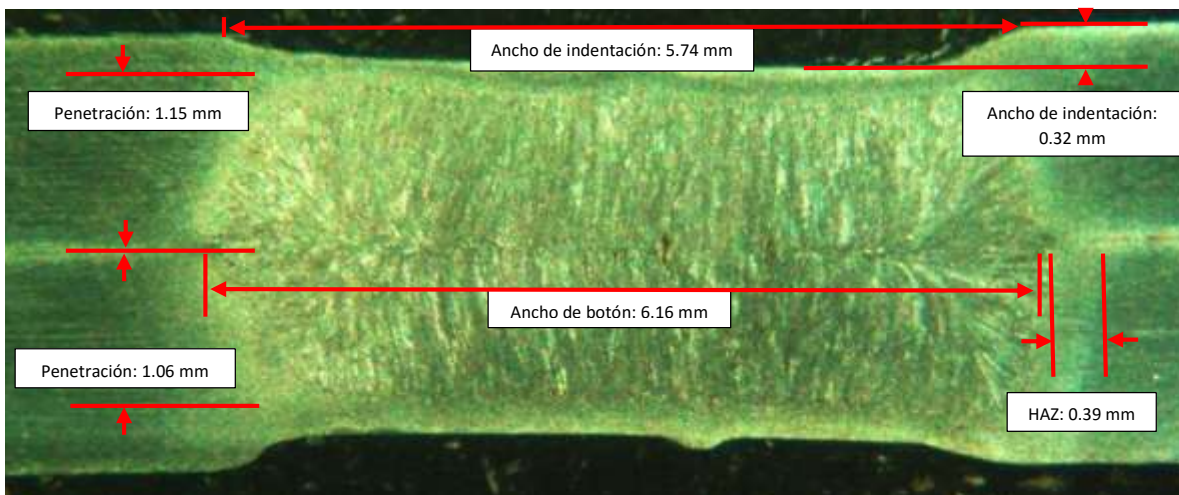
Mediciones realizadas en el botón de soldadura número 1.
